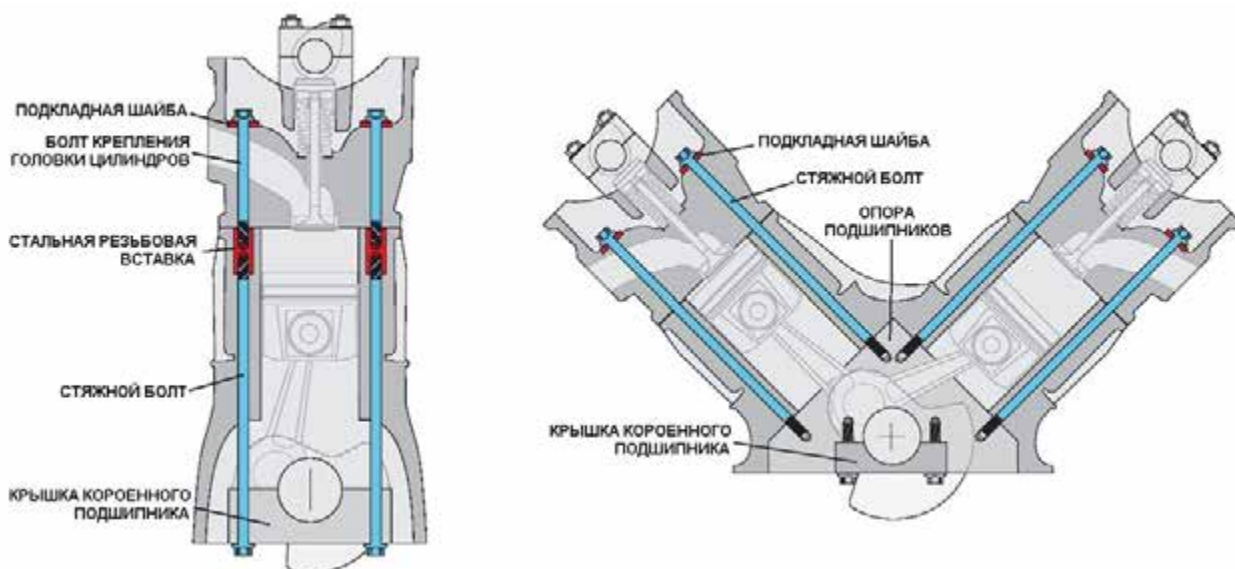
ro-21: Применение стяжных болтов и резьбовых вставок гарантирует защиту резьбовых отверстий блока цилиндров от повреждений; источник: MSI
